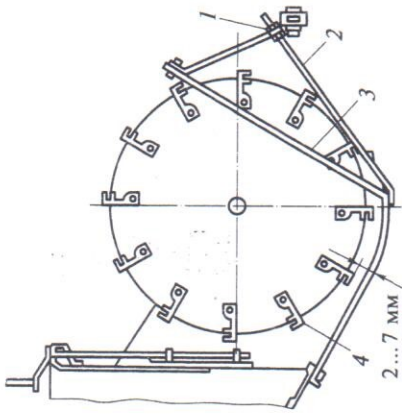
Регулировка зазора между ложечками и днищем питательного ковша:
